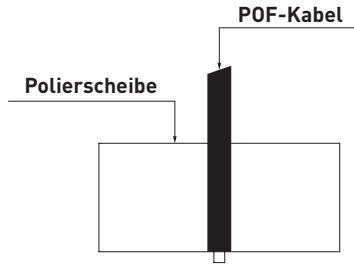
Polierscheibe mit Führung für die POF-Faser
